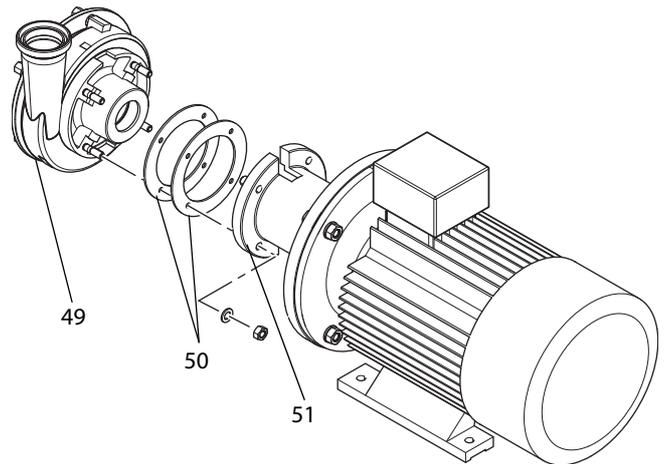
Spaltmaß bei Flanschverbindung einstellen
